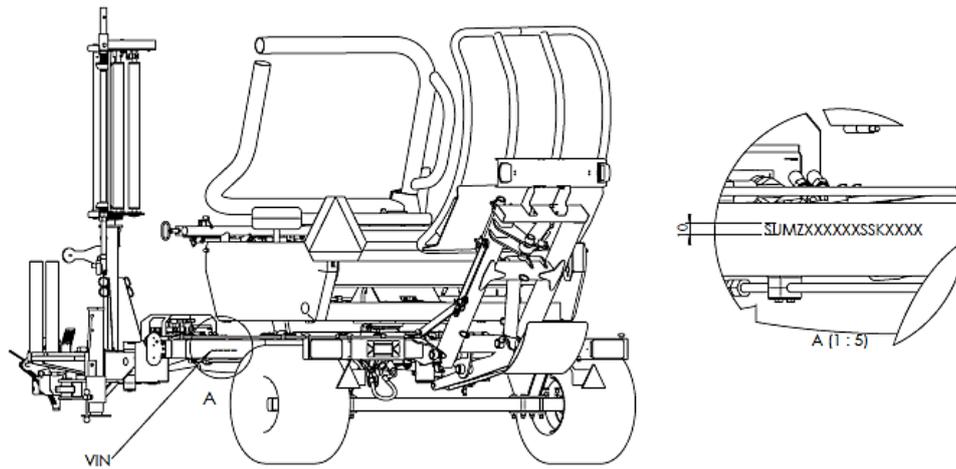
Emplacement de la plaque signalétique sur la machine
